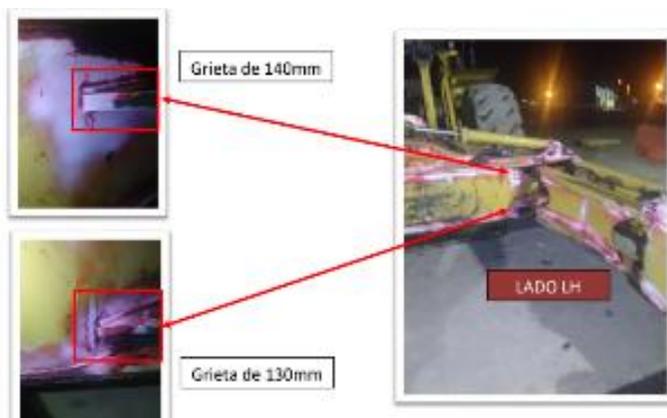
Grietas en la lámina frontal de los brazos de las pinzas lado izquierdo.
